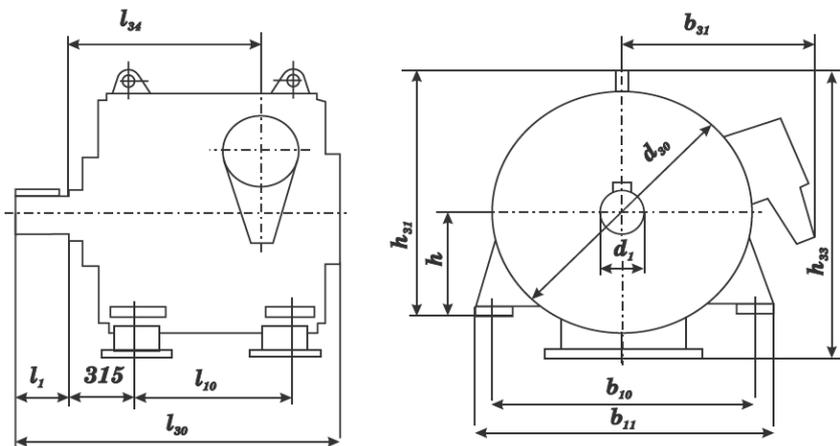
Габаритные, установочные, присоединительные размеры двигателей АКДЗ
